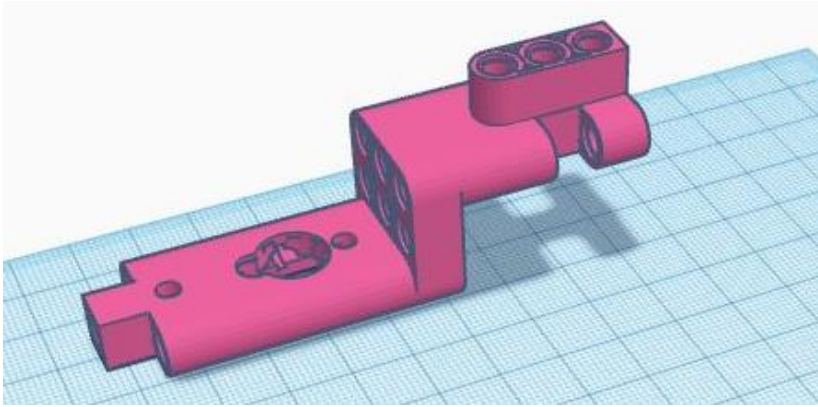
Распечатанные на 3D принтере крепления сервомашин
